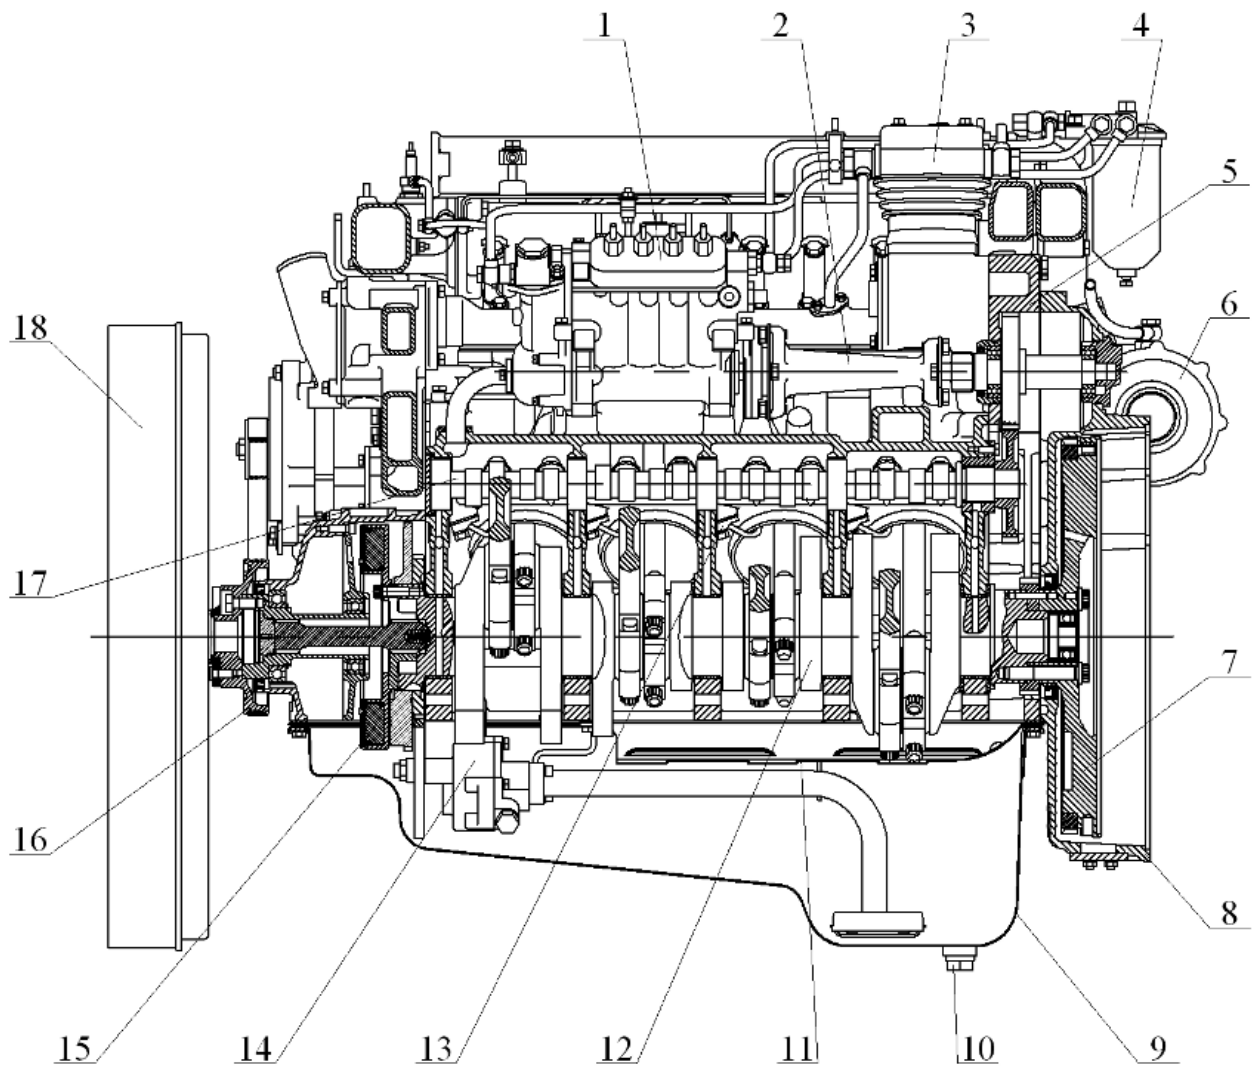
Продольный разрез двигателя с V-образным ТНВД «ЯЗДА»: 1 – топливный насос высокого давления (ТНВД); 2 – привод ТНВД; 3 – компрессор; 4 – фильтр тонкой очистки топлива; 5 – картер агрегатов; 6 – турбокомпрессор; 7 – маховик; 8 – картер маховика; 9 – картер масляный; 10 – пробка слива масла; 11 – желоб маслораспределительный; 12 – коленчатый вал; 13 – форсунка охлаждения поршня; 14 – масляный насос; 15 – гаситель крутильных колебаний; 16 – шкив коленчатого вала; 17 – вал распределительный; 18 – вентилятор с муфтой
